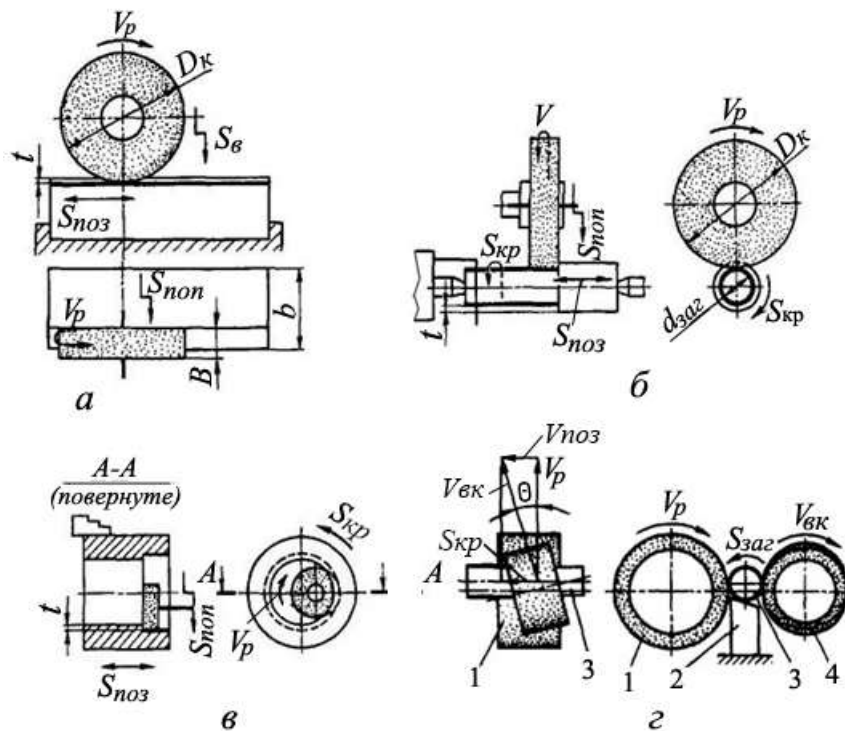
Схеми обробки на шліфувальних верстатах
